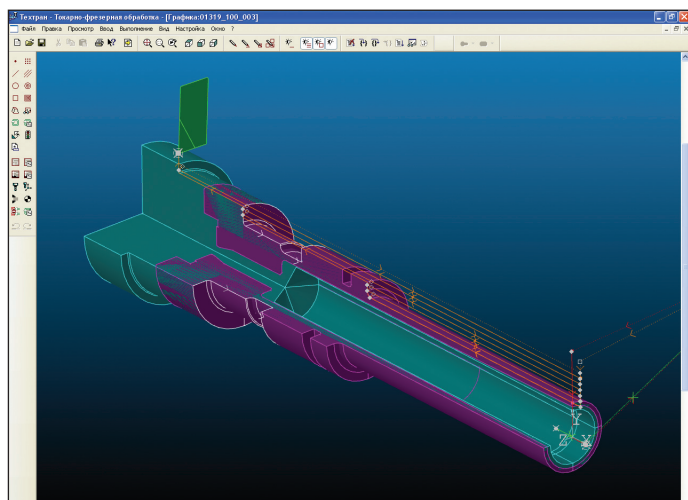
Частичный разрез детали и заготовки (произвольный вид)
